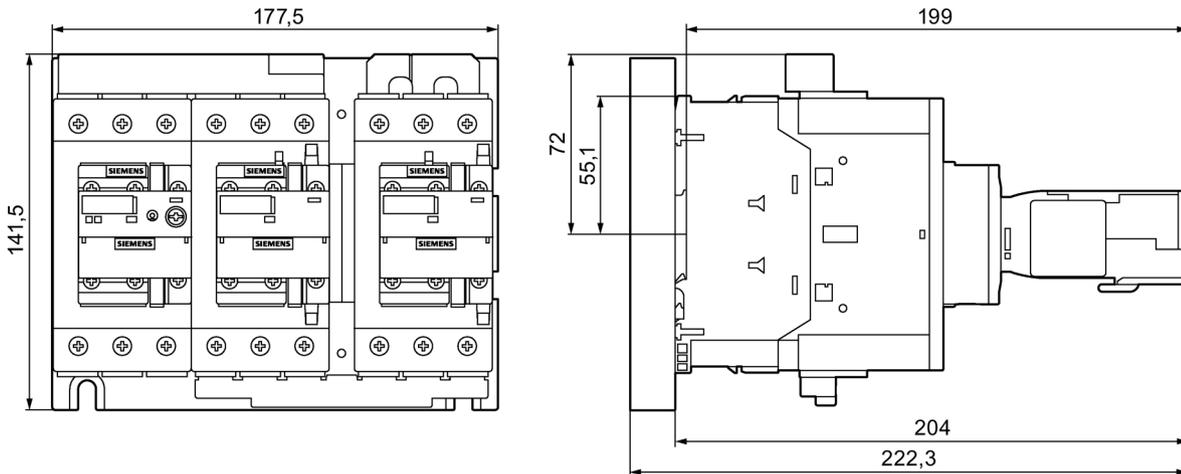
Ensembles étoile-triangle 3RA2437-8X.32-1 (S2-S2-S2) sur plaque de montage
